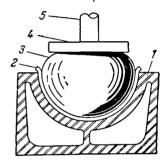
Схема прессования с упругим пуансоном: 1—матрица; 2—заготовка из пропитанной свизующим стеклоткани; 3—пуансон; 4—верхняя плита; 5—плунжер пресса.
